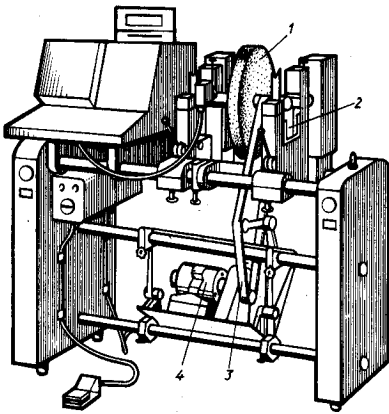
Станок ДБ-10 для динамической балансировки: 1 – ротор; 2 – опоры станка; 3 – ременный привод от электродвигателя 4 к балансировочной оправке
